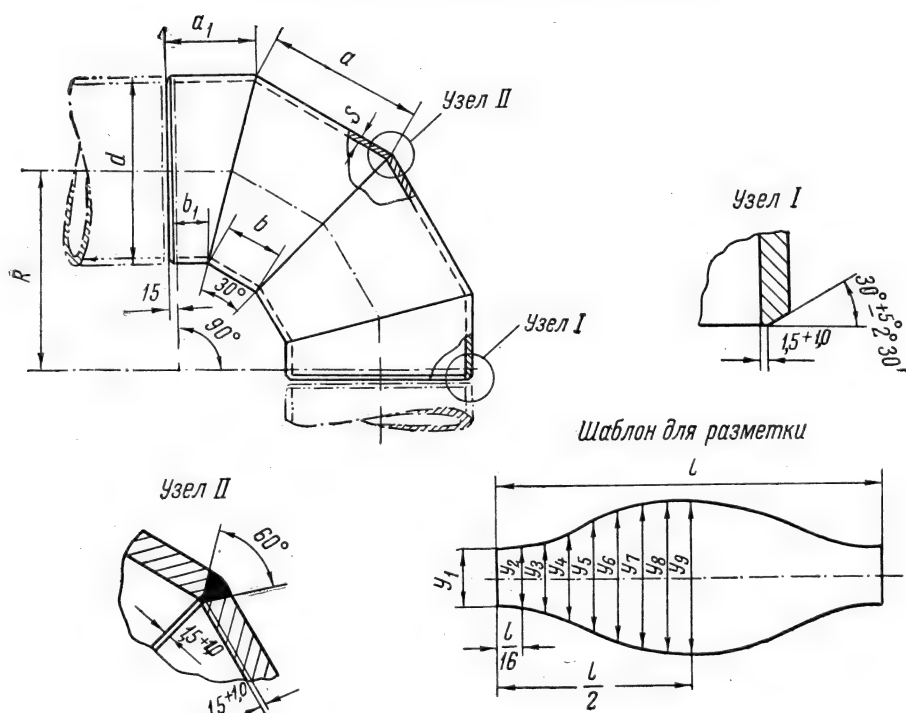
Отвод сварной с углом поворота 90° .
